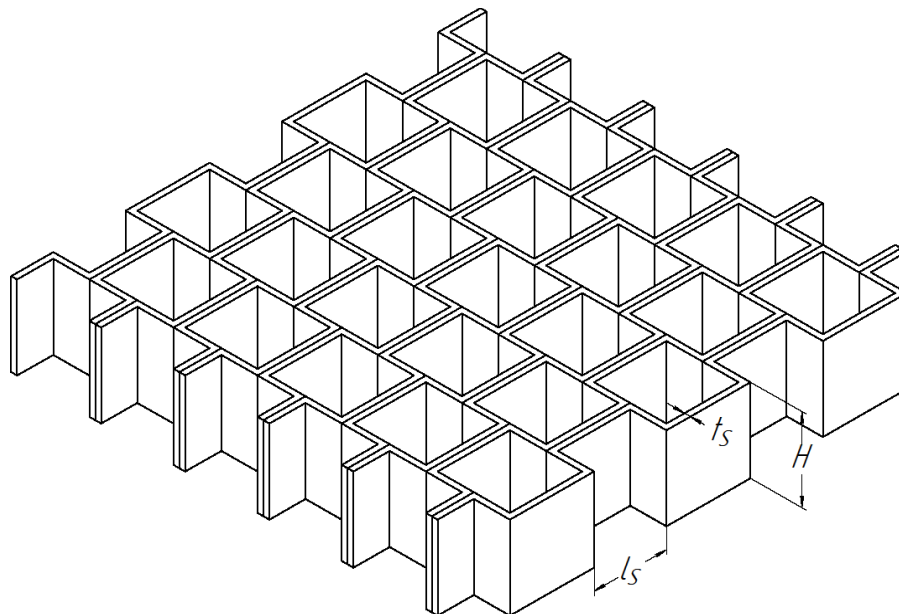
Сотовый наполнитель с квадратными ячейками.
